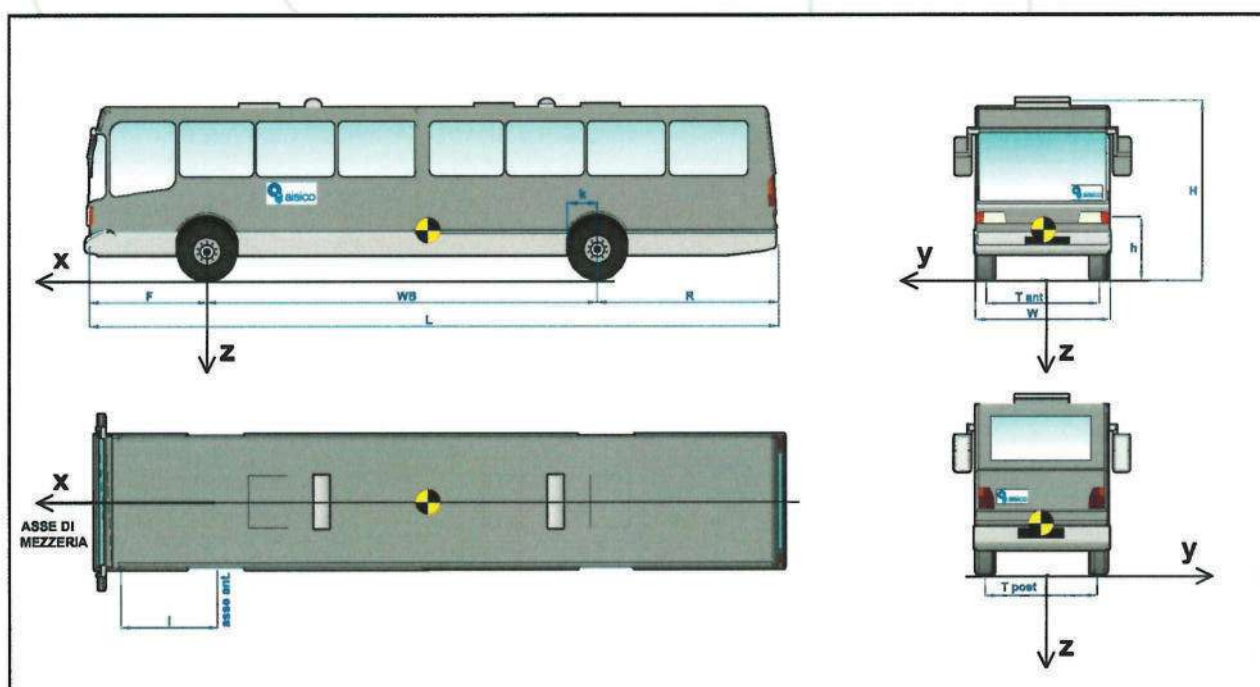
Figure 3 Dimensioni del veicolo – Vehicle dimensions
